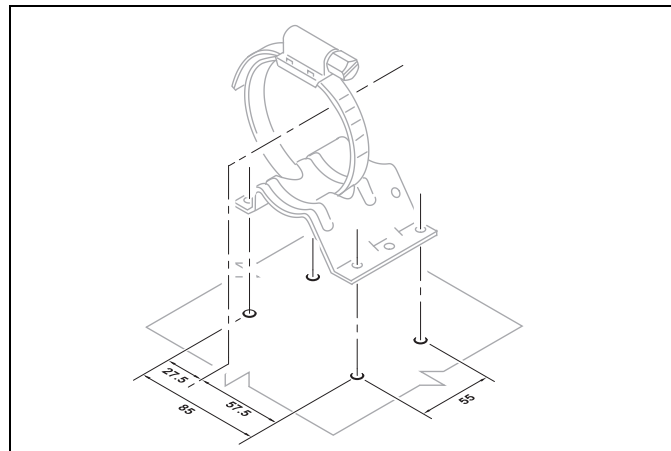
Схема расположения отверстий для установочного кольца циркуляционного насоса U 4854
